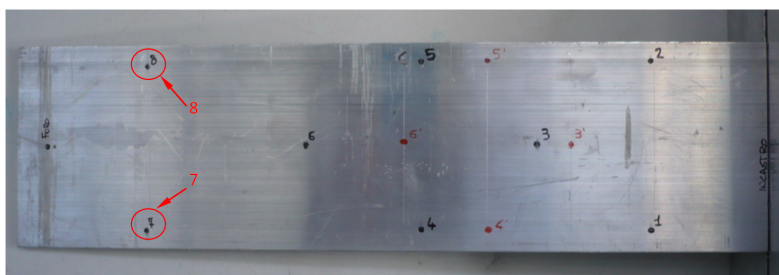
Punti di contatto degli LVDT utilizzati nella prova con la piastra piana in alluminio.
